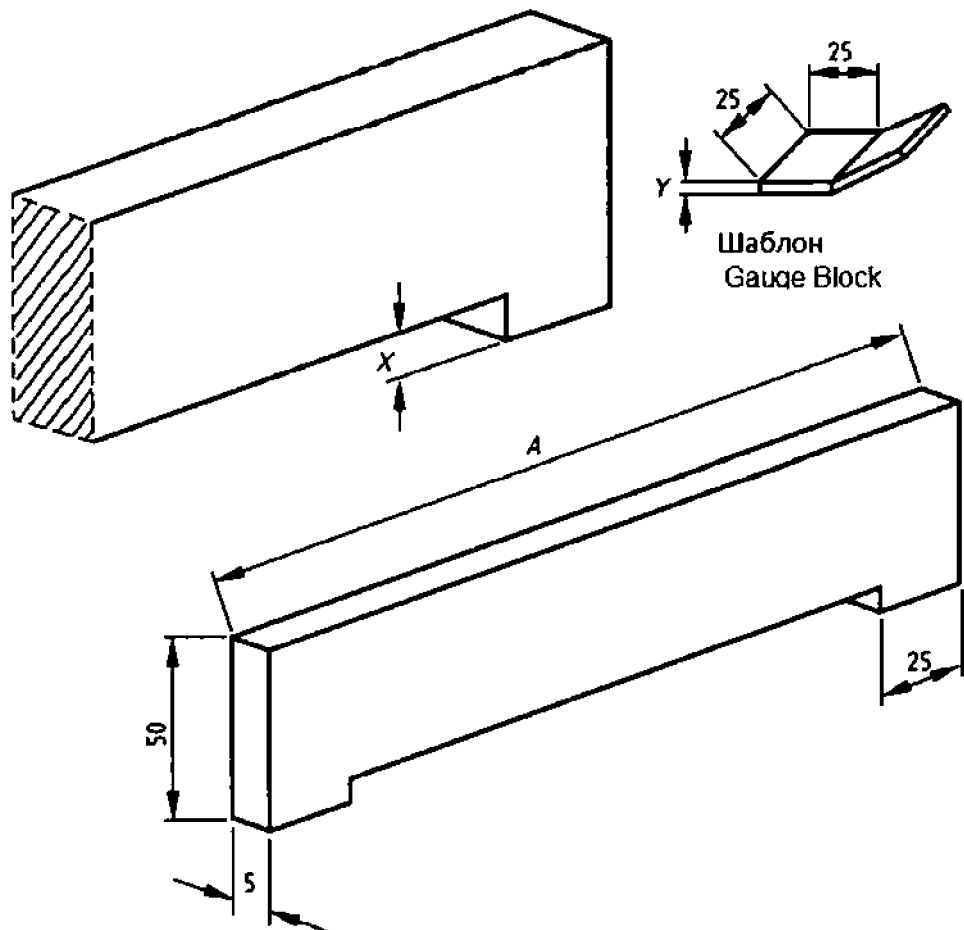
Приклад вимірювальної лінійки з вирізом на кромці і вимірювальної пластини
